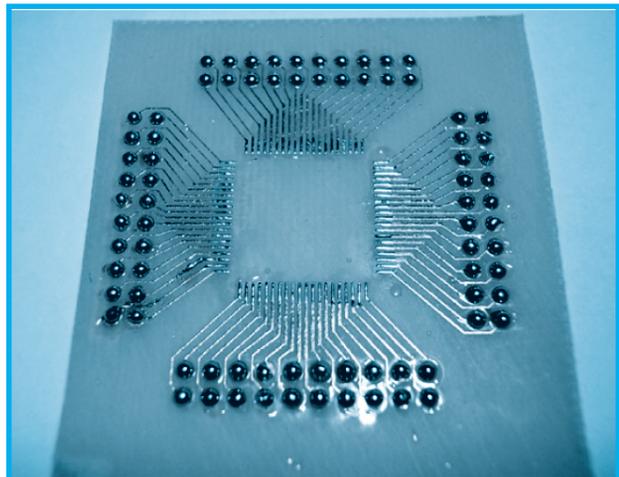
Antes de soldar un integrado con muchas patas debe estañar las pistas del PCB donde se ubicará el componente.
